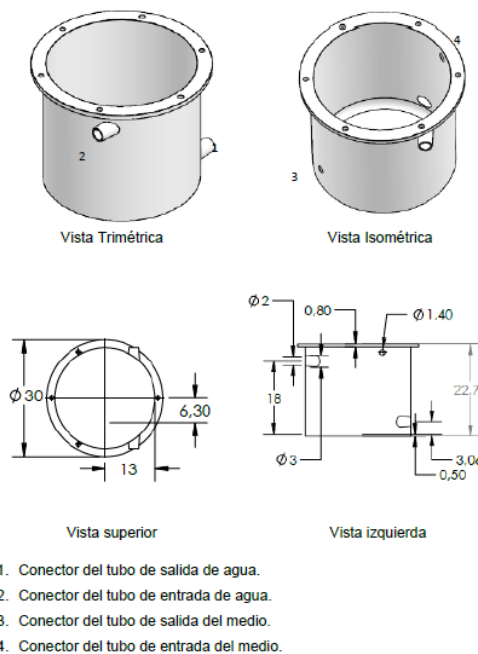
Dimensiones del enchaquetado (Diseño en SolidWorks2017®)
